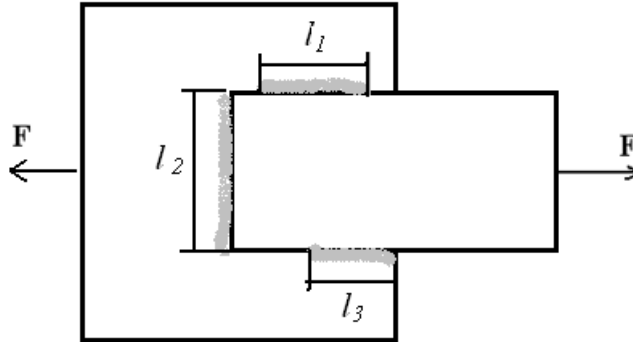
Soudure à clin ou à couvre joints cas combiné
